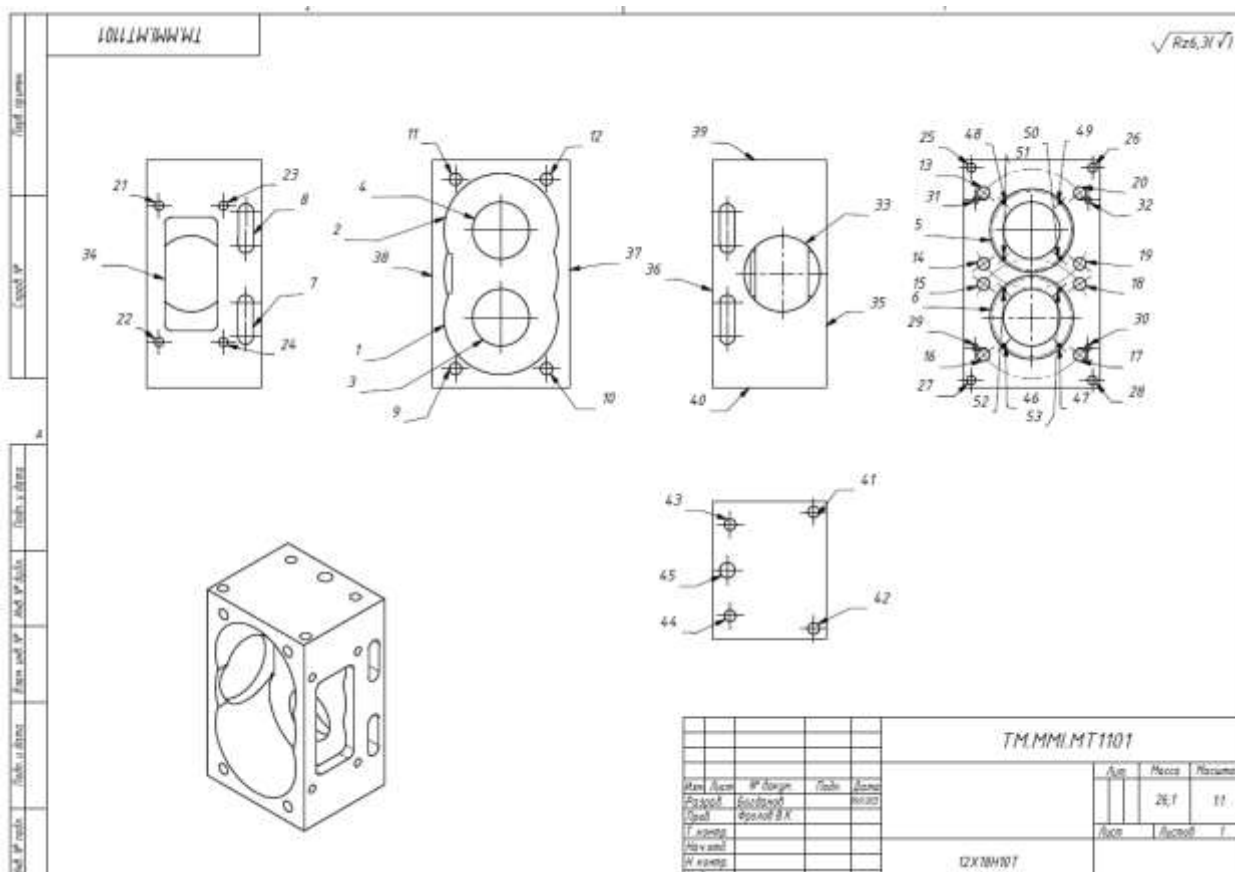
Позначення поверхонь деталі «Корпус насоса»
